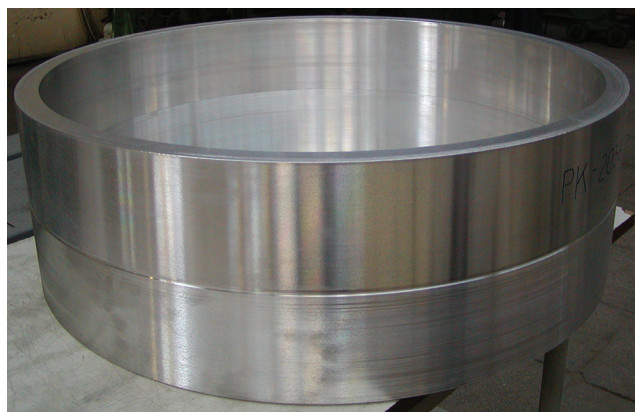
Заготовки для сварки из раскатных колец сплава В-1469
